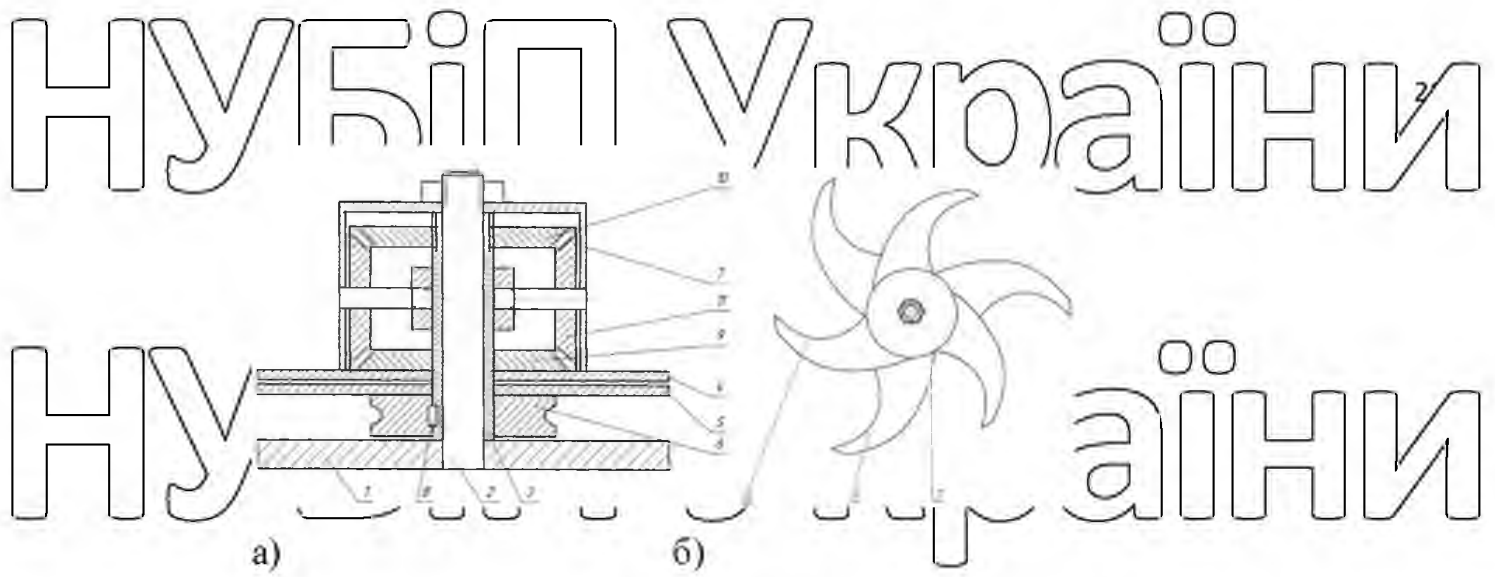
Універсальний дводисковий ріжучий апарат: а) вид сбоку; б) вид
